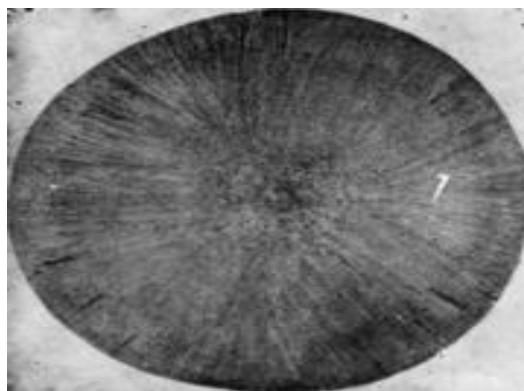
травленный темплет круглой непрерывнолитой заготовки
